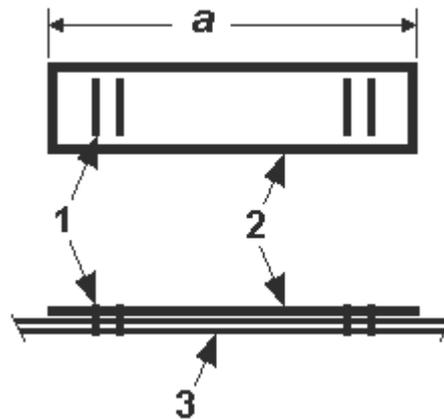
Patrón de corte de la funda (fundas exterior e interior)
